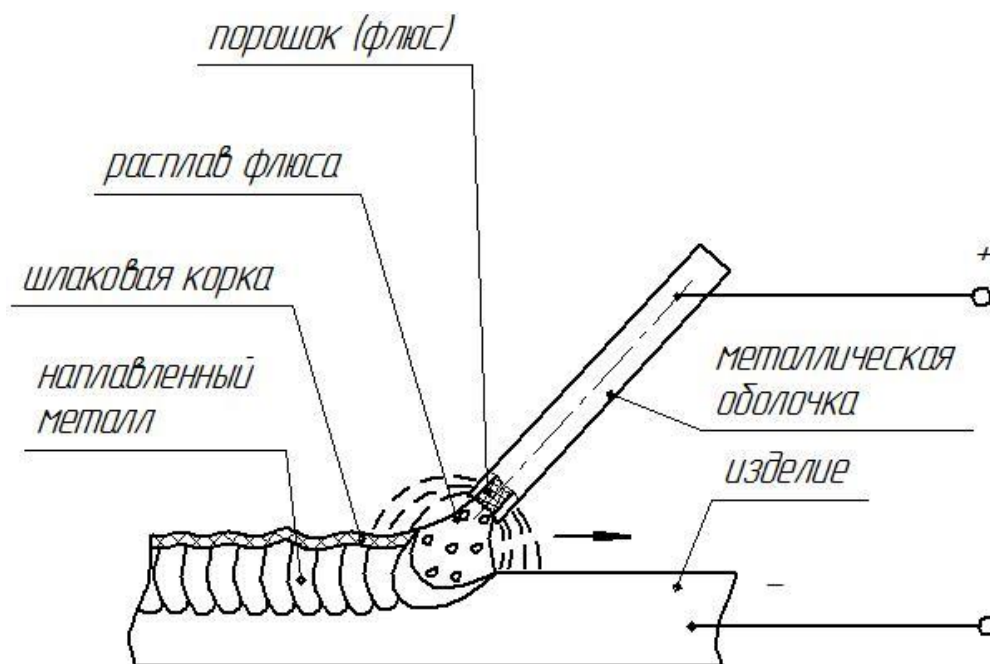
Схема осуществления сварки самозащитной порошковой проволокой
